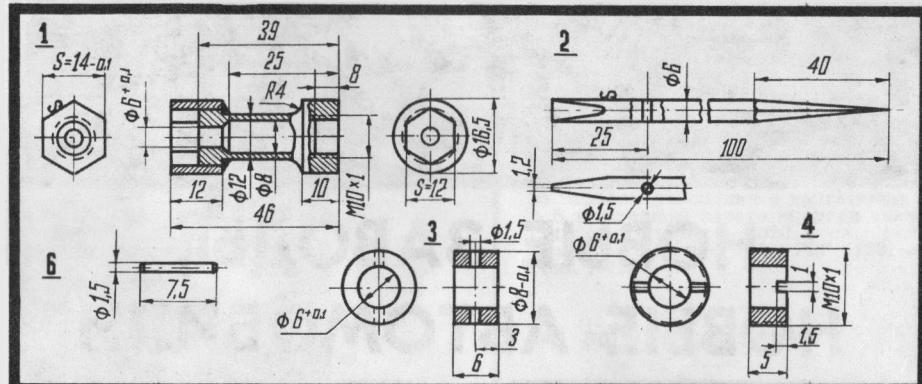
Детали ключа-отвертки. Обозначения те же, что и на рис. 1
